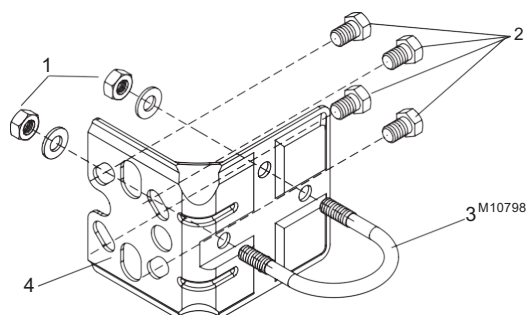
Детальный вид монтажного кронштейна, В2, для установки на трубу и стену.
